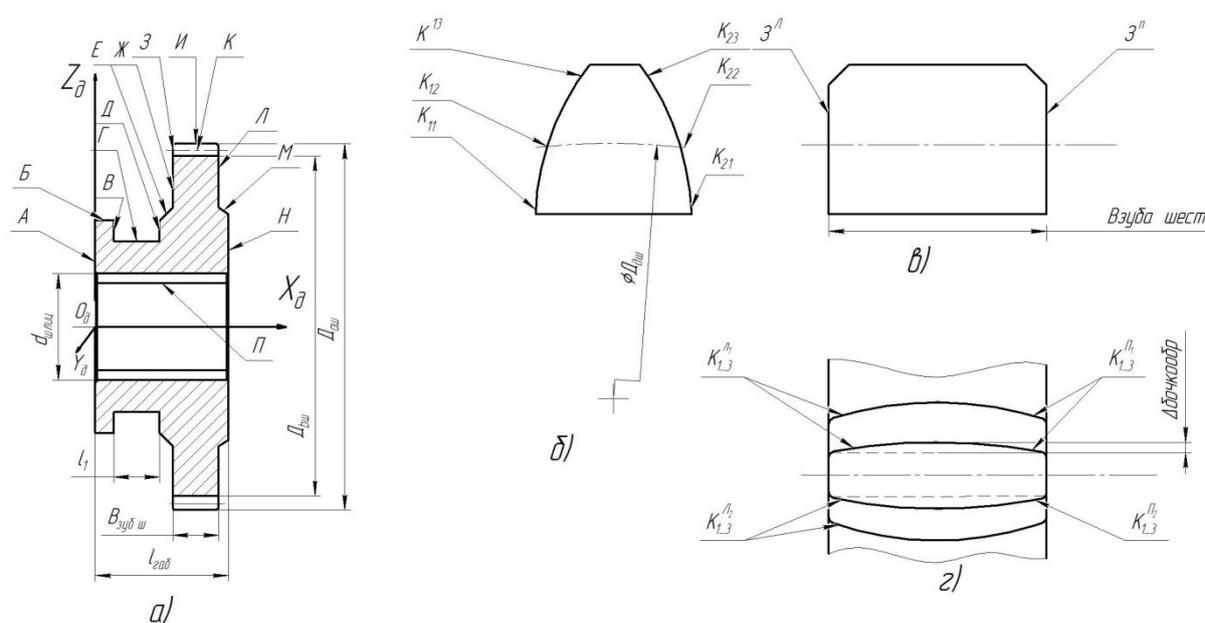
Эскиз ведущей шестерни КПП без прерывания потока передаваемой мощности
